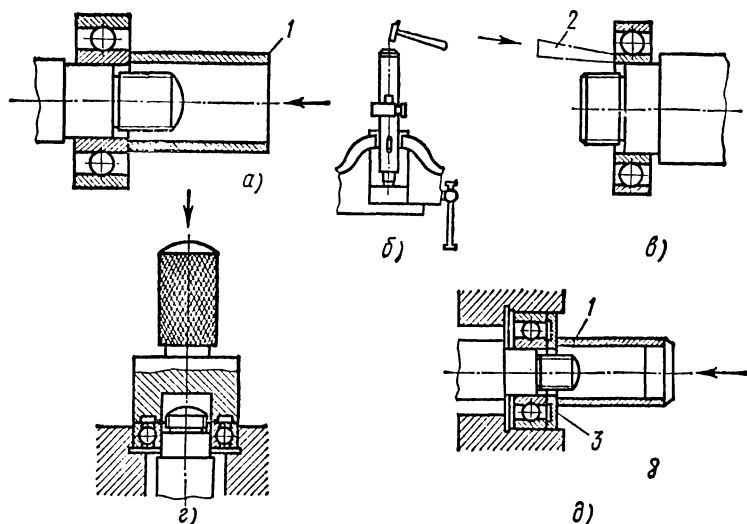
Способы монтажа и демонтажа подшипников качения:
